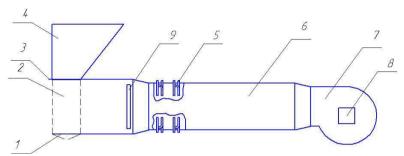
Схема макета установки для тепловой обработки зерна:
